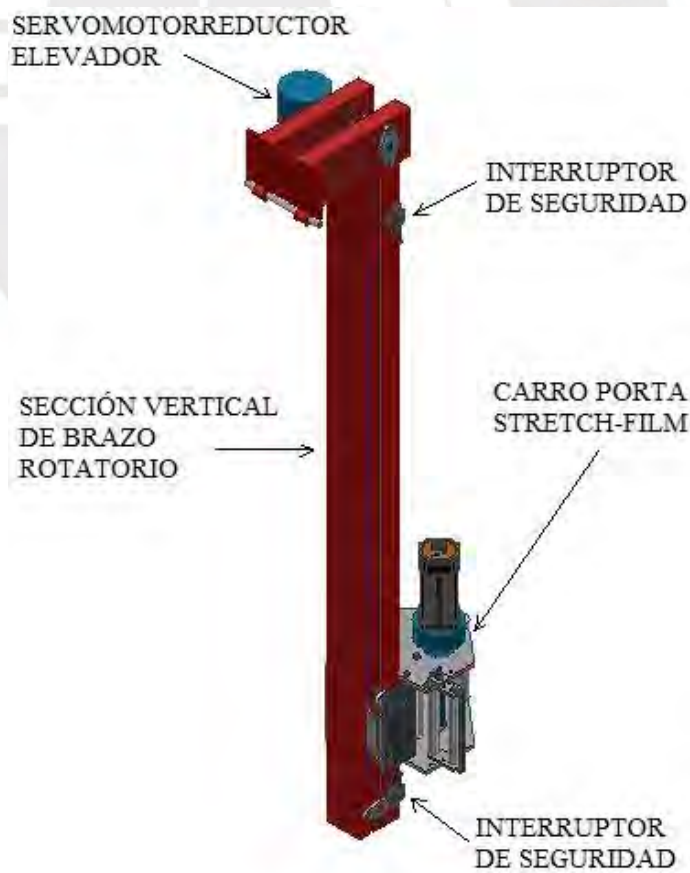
Estructura vertical de brazo giratorio. Fuente: Propia.
